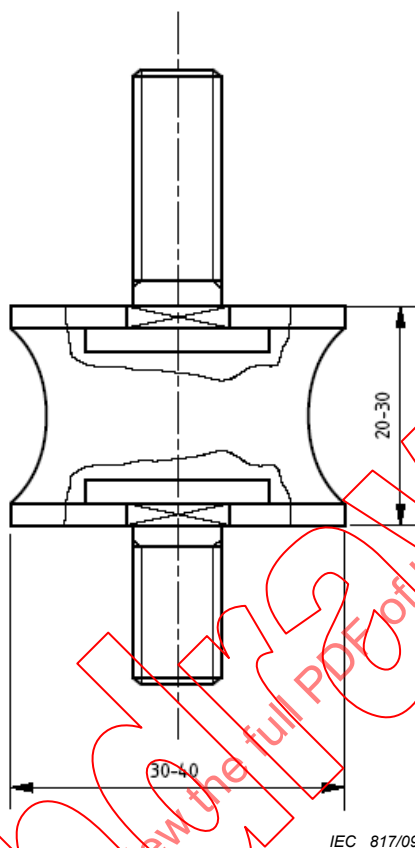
Manchon amortisseur type en caoutchouc pour supporter l'échelle d'essai
